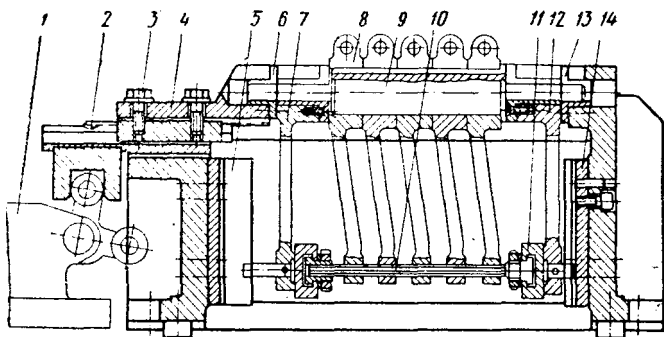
Универсально-наладочное приспособление для обработки паза зажима в рычагах
